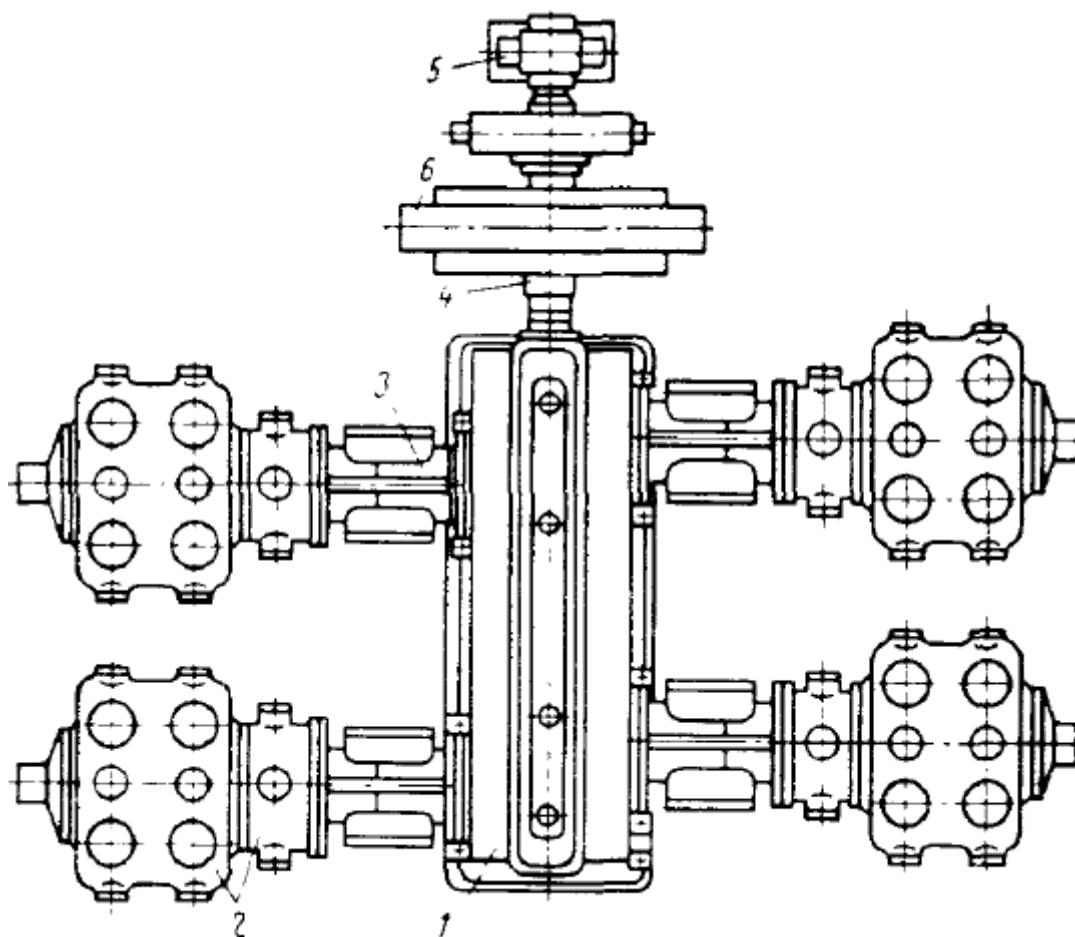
Горизонтальний опозитний чотирирядний багатоступінчастий компресор: 1 – рама; 2 – циліндри; 3 – напрямні крейцкопфів; 4 – колінчастий вал; 5 – виносний підшипник; 6 – електродвигун [10].
